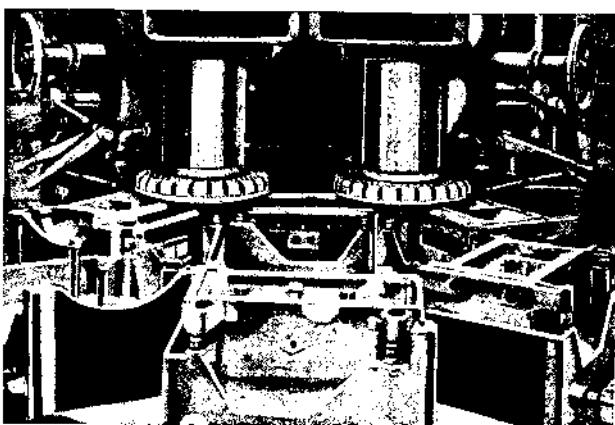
Фрезеровка нижней поверхности блока Моррис.
